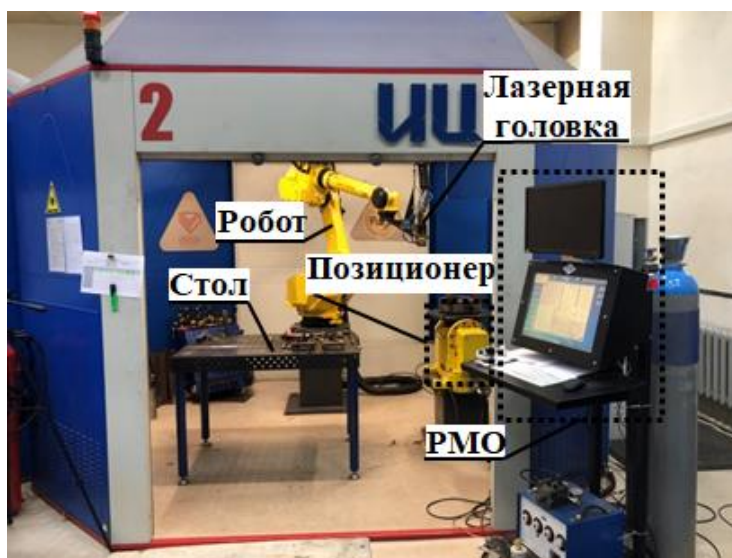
Лазерный роботизированный комплекс сварки центра НОЦ ВЛТ ВлГУ
